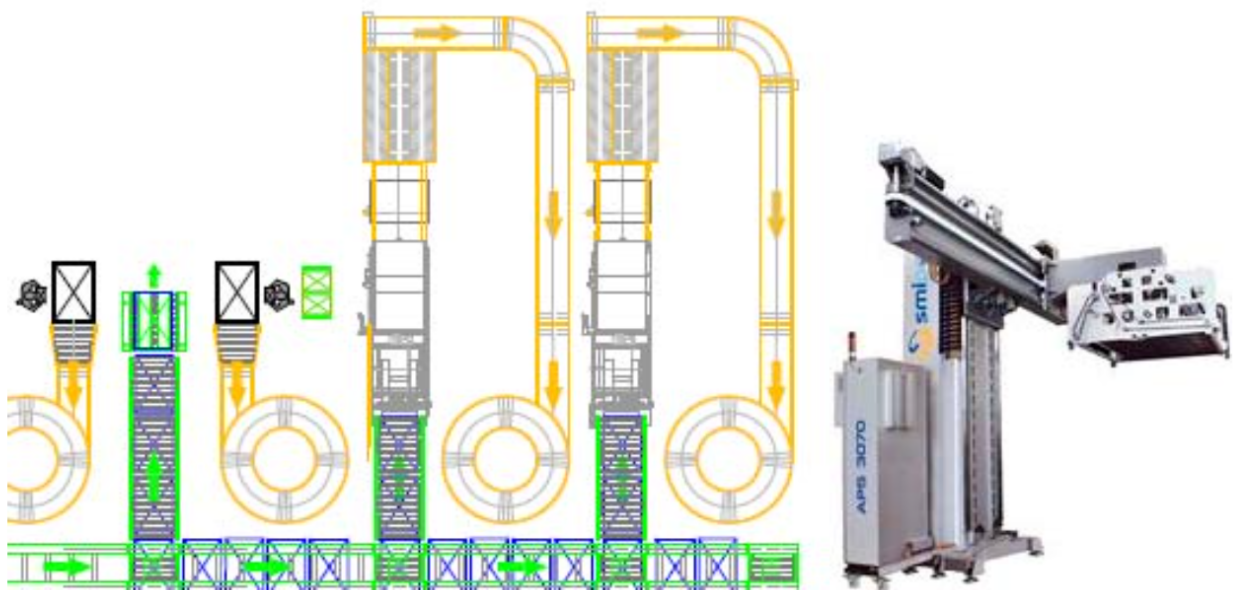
Despaletizador asistido (izquierda) y automático de capas o pilas (derecha) Fuente Elaboración propia
